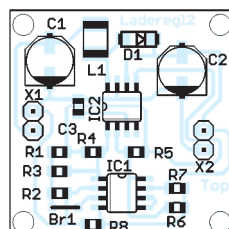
Layout der Platine des Ladereglers nach Bild 5; Abmessungen 35 mm x 28 mm, M 1:1
